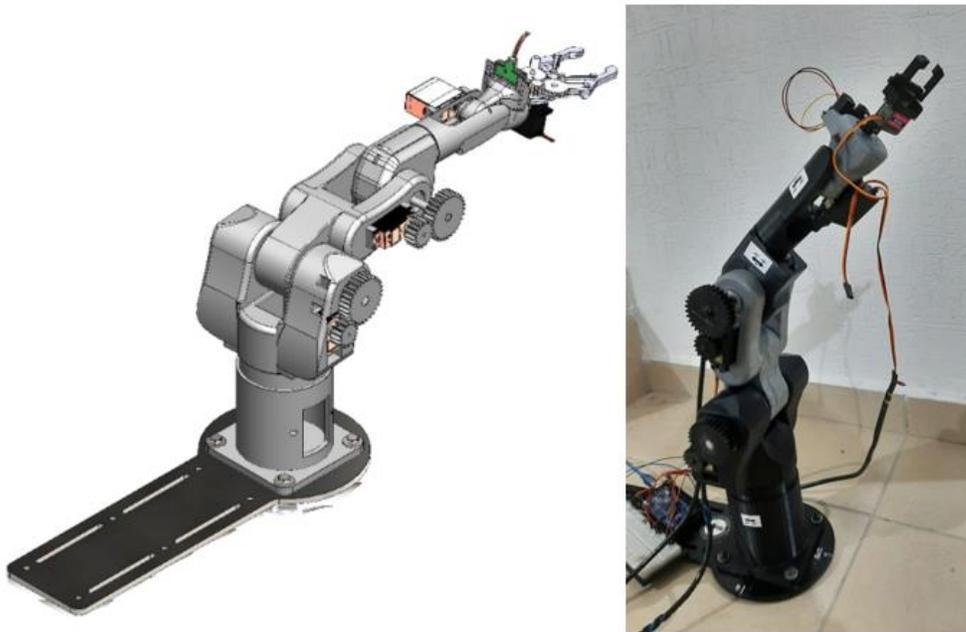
Vista de Diseño en Cad y Vista Real del Robot
